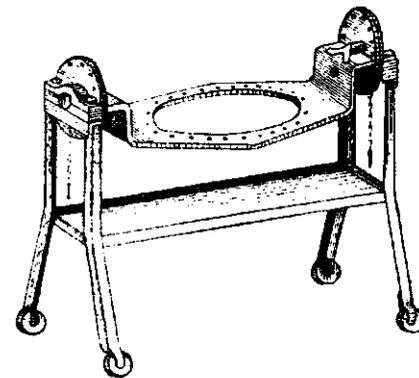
Приспособление для разборки и сборки нагнетателя мотора М-34.
